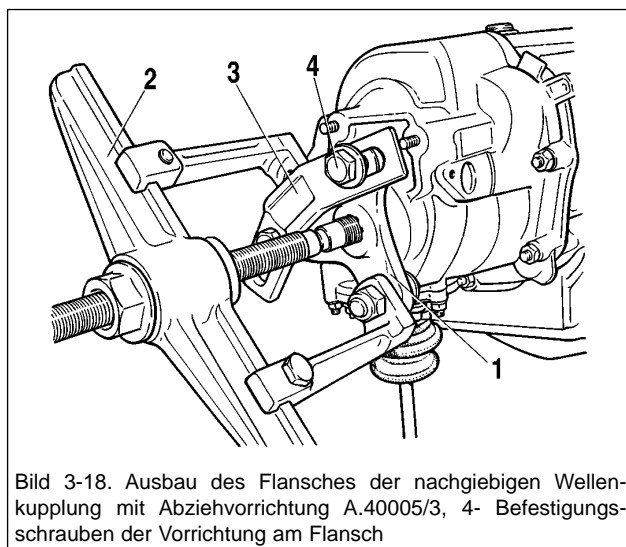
Ausbau des Flansches der nachgiebigen Wellenkupplung mit Abziehvorrichtung A.40005/3, 4- Befestigungsschrauben der Vorrichtung am Flansch
